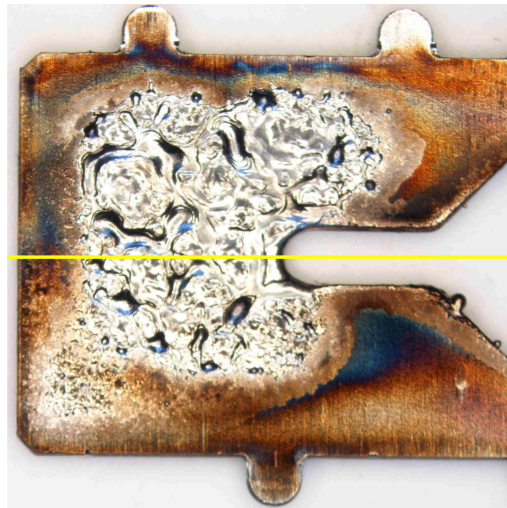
Position du plan de coupe (trait jaune) sur une plaquette de fractionnement.
